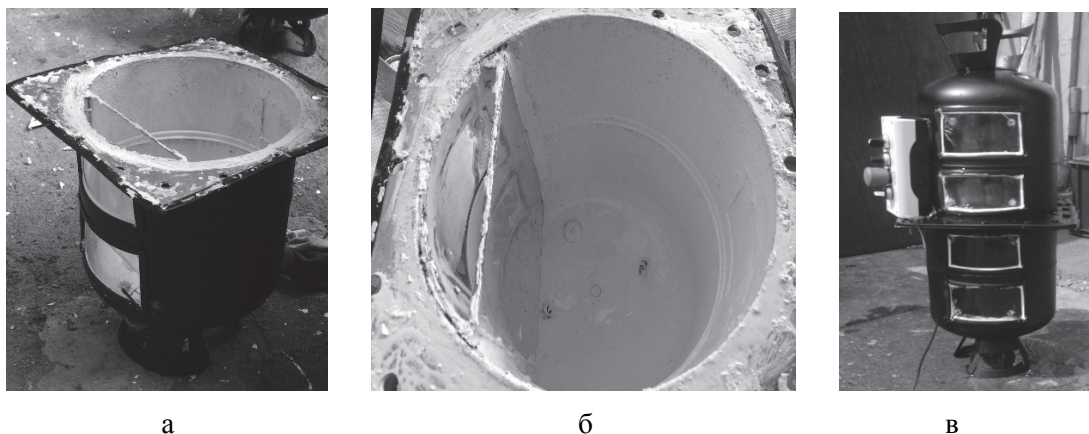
Покрытие корпуса установки антикоррозийной краской: а – нижний резервуар; б – верхний резервуар; в – общий вид
